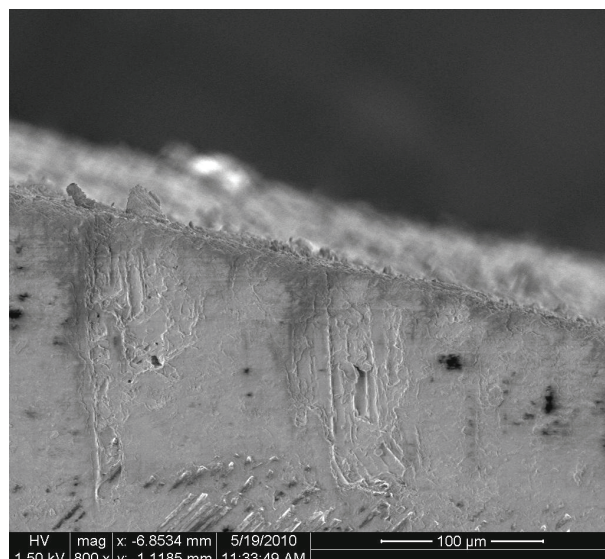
Вид кромки отверстия в образце, упрочненной наноклеевой композицией
